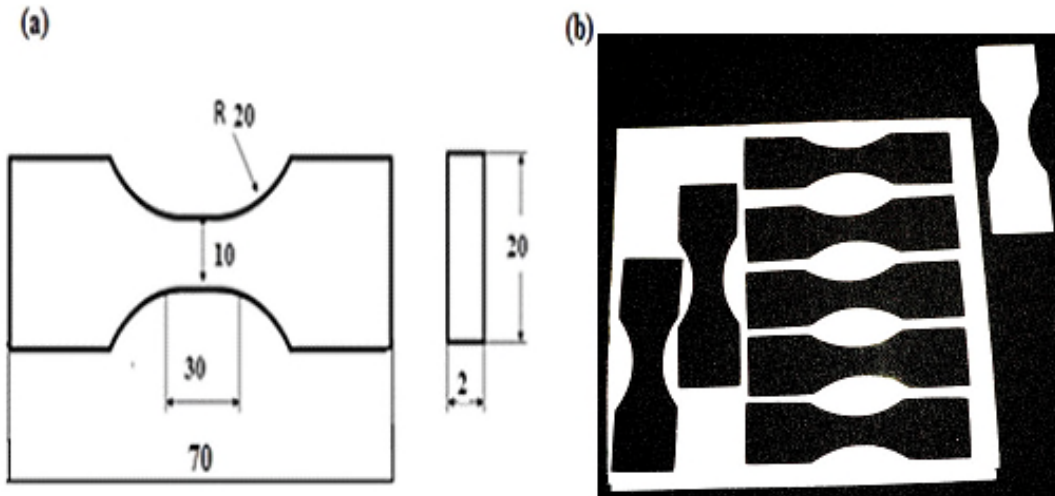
Géométrie des éprouvettes du PBT/PTMO
